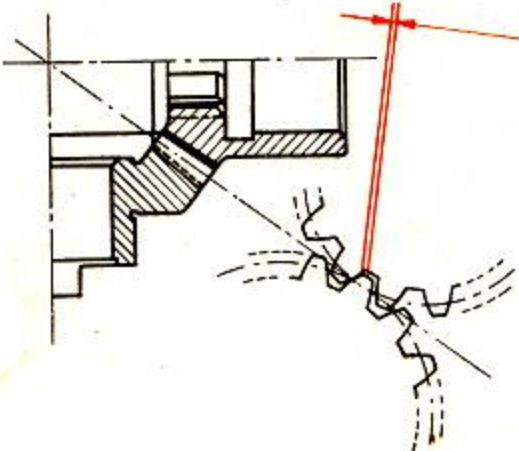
Acople de los engranajes cónicos del árbol motor
